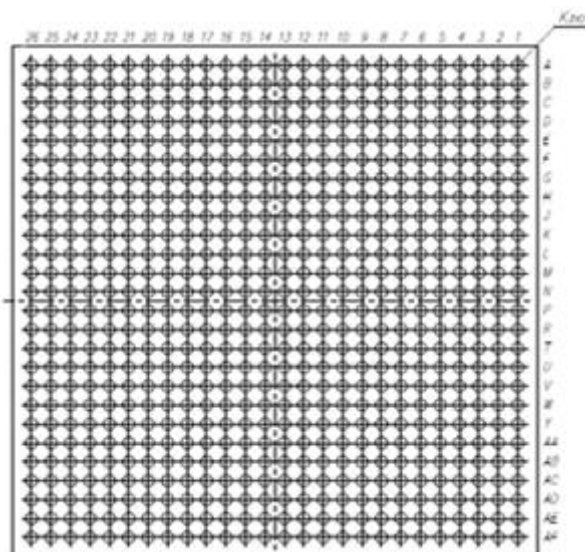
Корпус СБИС МИ БИУС, вид со стороны выводов
